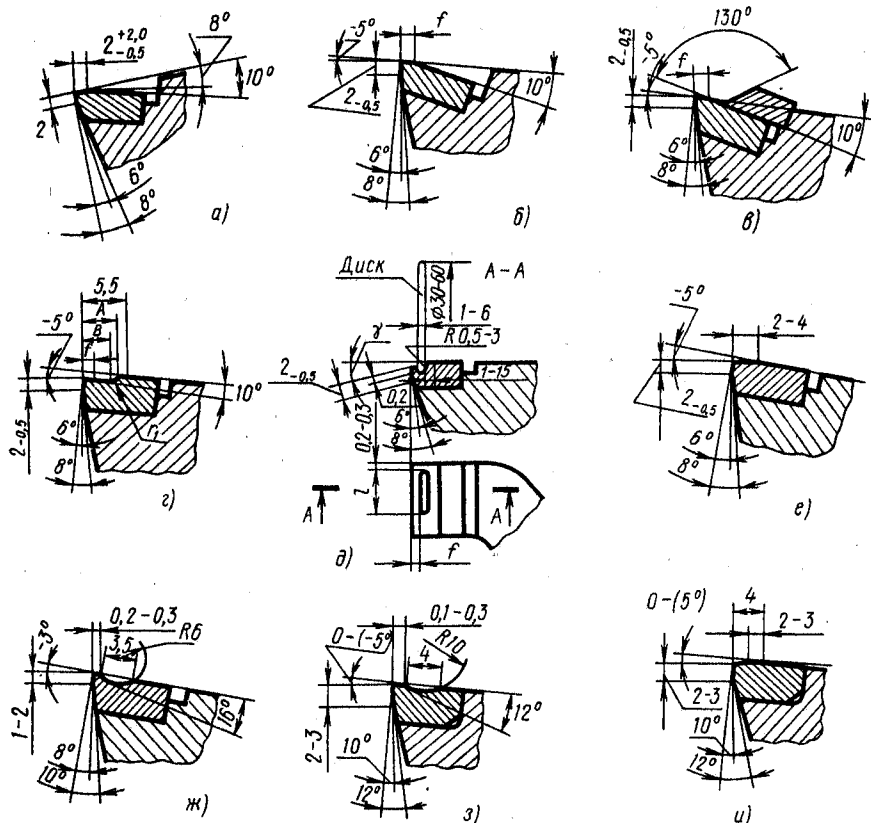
Формы передней поверхности резцов с твердосплавной пластинкой
